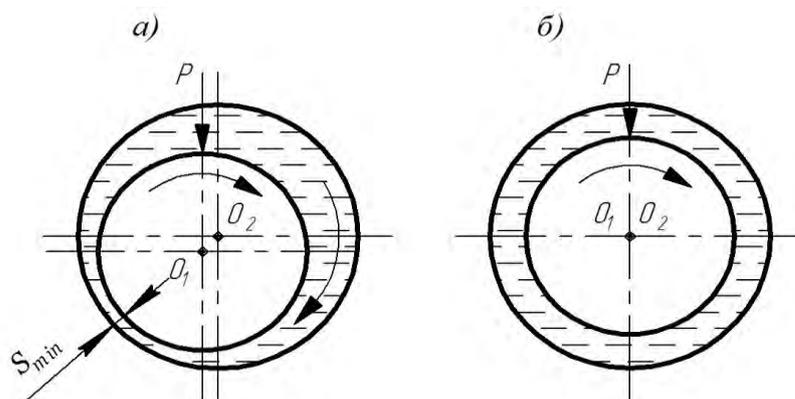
Схема формирования масляного клина в подшипнике скольжения коленчатого вала: O_1 – центр шейки коленчатого вала; O_2 – центр подшипника
